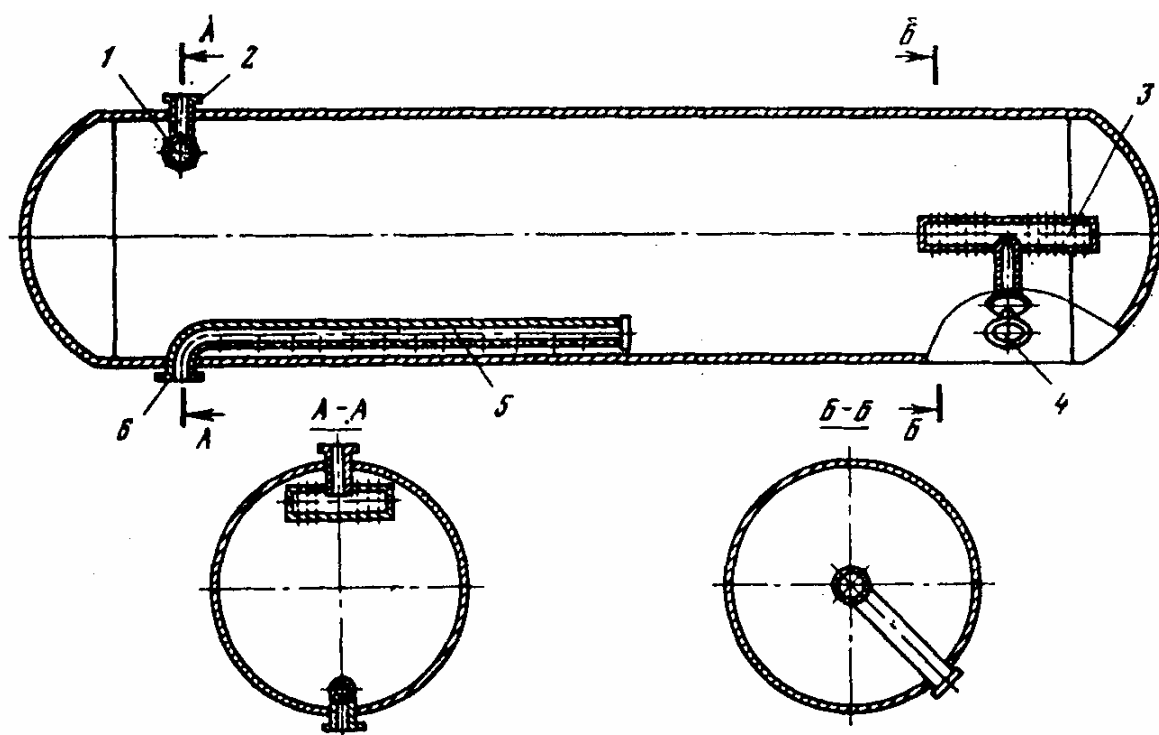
Общий вид отстойника ОБН-3000/6
